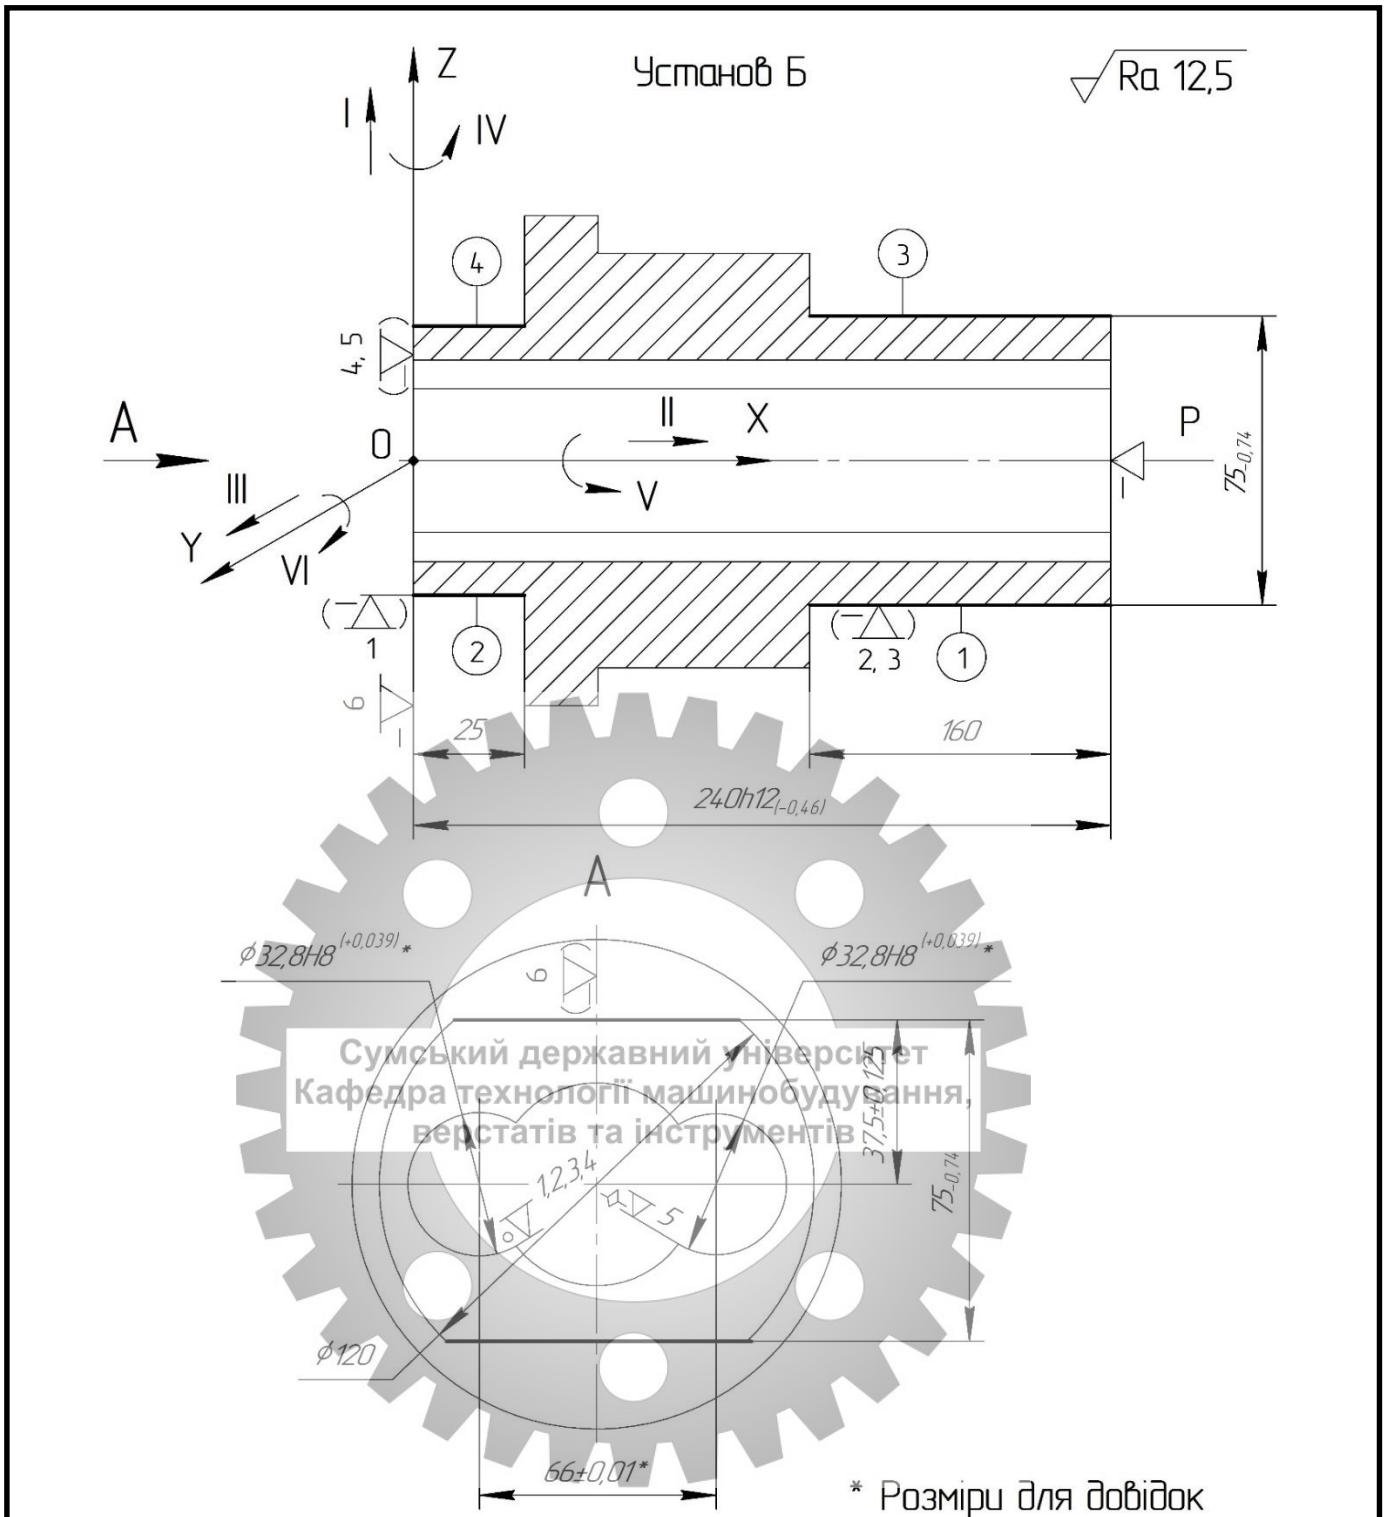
Схема базування заготовки на операції 025, схема №1. В дужках схема №2
